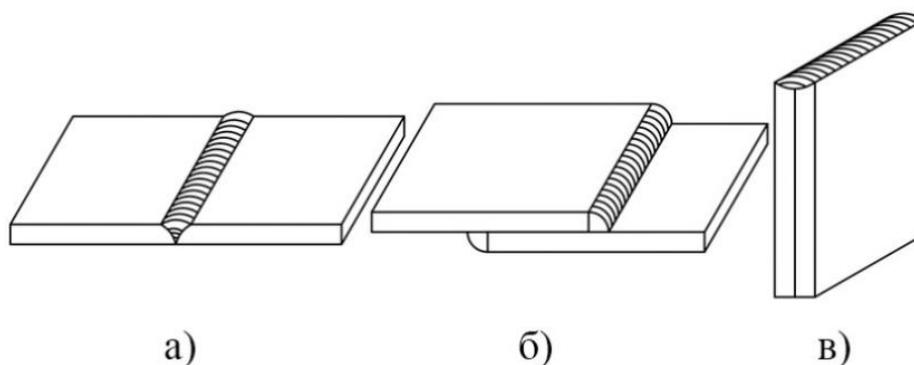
Типы сварных швов: а) стыковой; б) нахлесточный; в) торцевой
